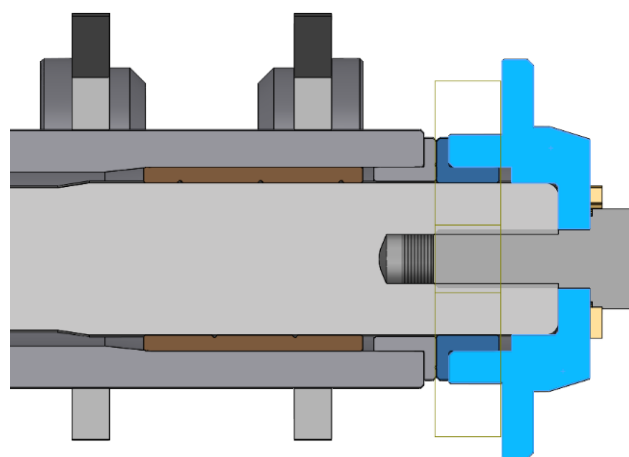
Ajustamento entre apoio da cavilha e anilha de desgaste (chassi).
